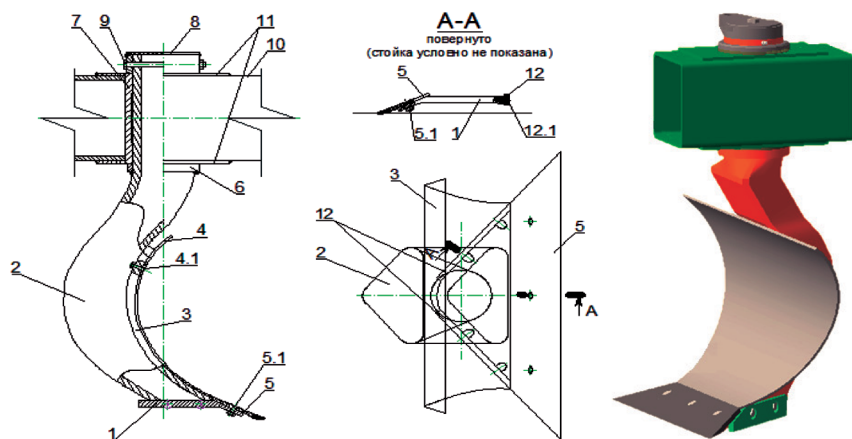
Симметричный ромбовидный корпус рабочего органа поворотного плуга
